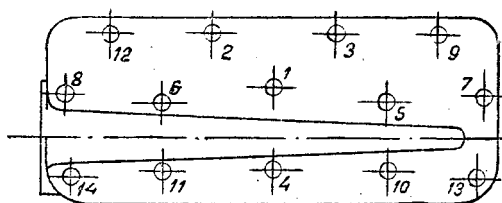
Порядок затяжки гаек головки цилиндров двигателя М-1.
